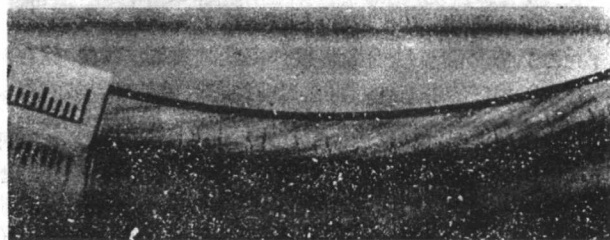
GCr15SiMn 轴承外圈磨削裂纹宏观形貌
